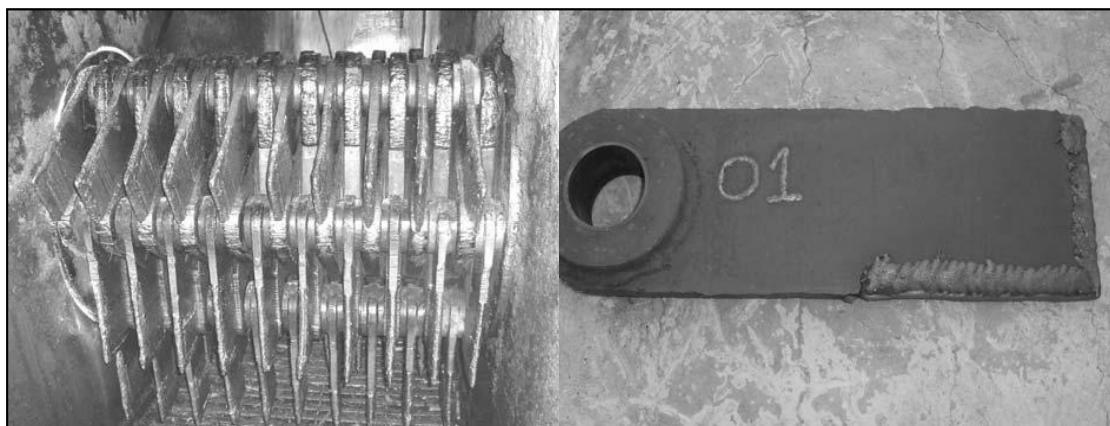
Vista Interna do Picador e Detalhe de Uma Faca Picadora.
